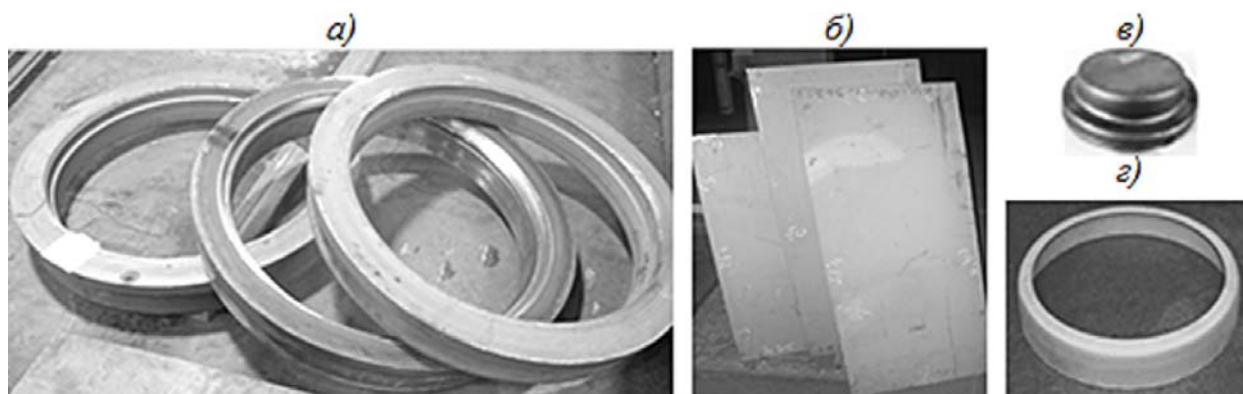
Полуфабрикаты и детали из сплава ВЖ172: *а* – цельнокатаные кольцевые заготовки массой 240 кг; *б* – листы; *в* – штамповка детали «фланец» камеры сгорания; *г* – деталь «обечайка» камеры сгорания
